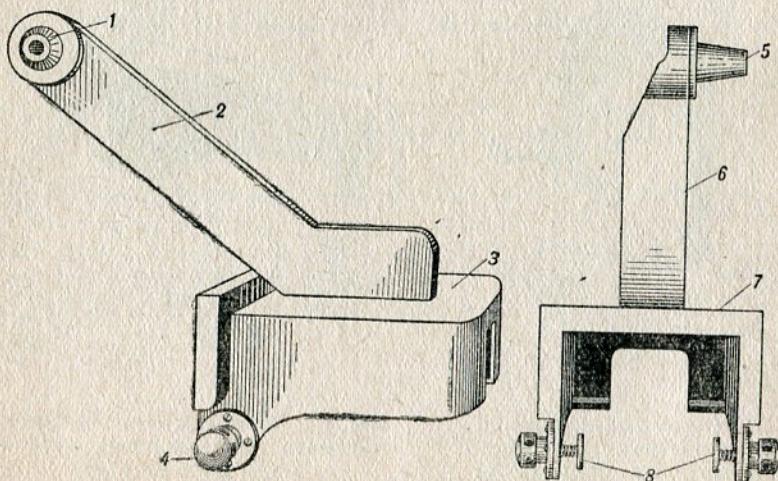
Остов для крепления фотокинопулемета на спаренной подвижной пулеветной установке (вид сбоку и спереди)
